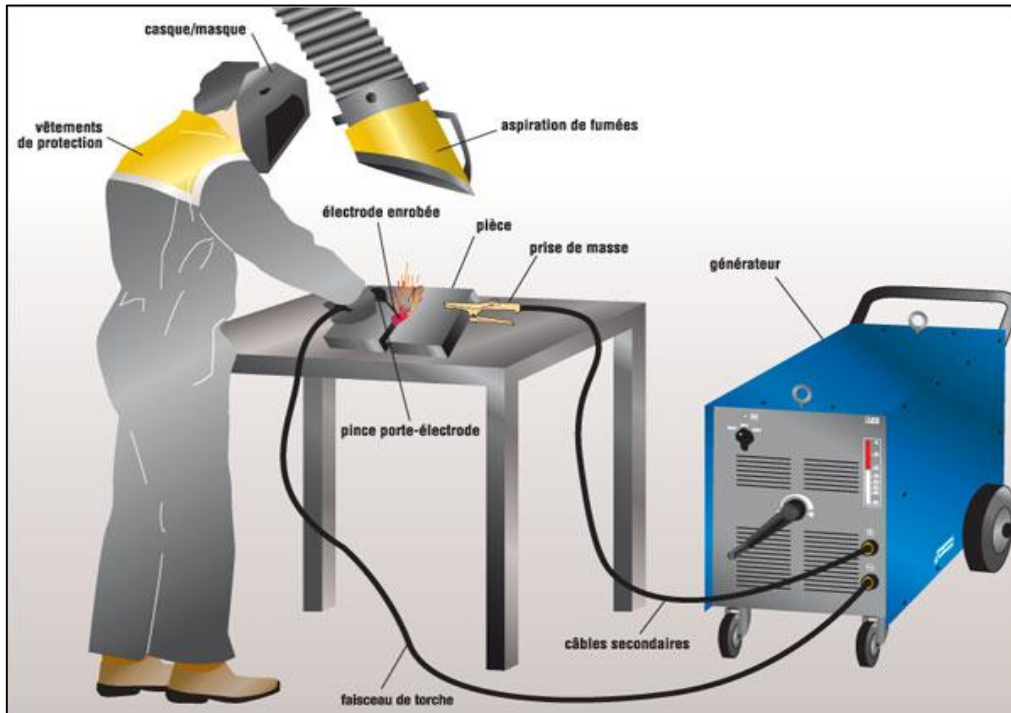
Soudage par électrode enrobée [17]
